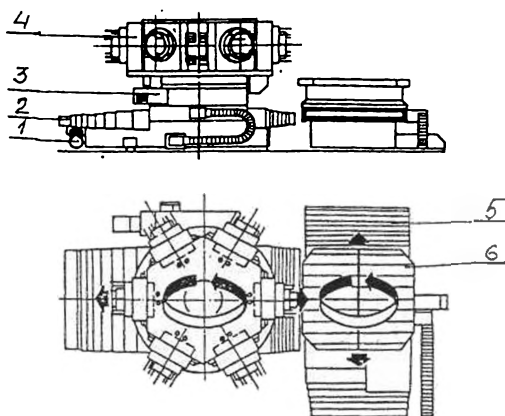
Компонівка агрегатного верстата з ЧПУ і змінними багатопшпіндельними головками:
